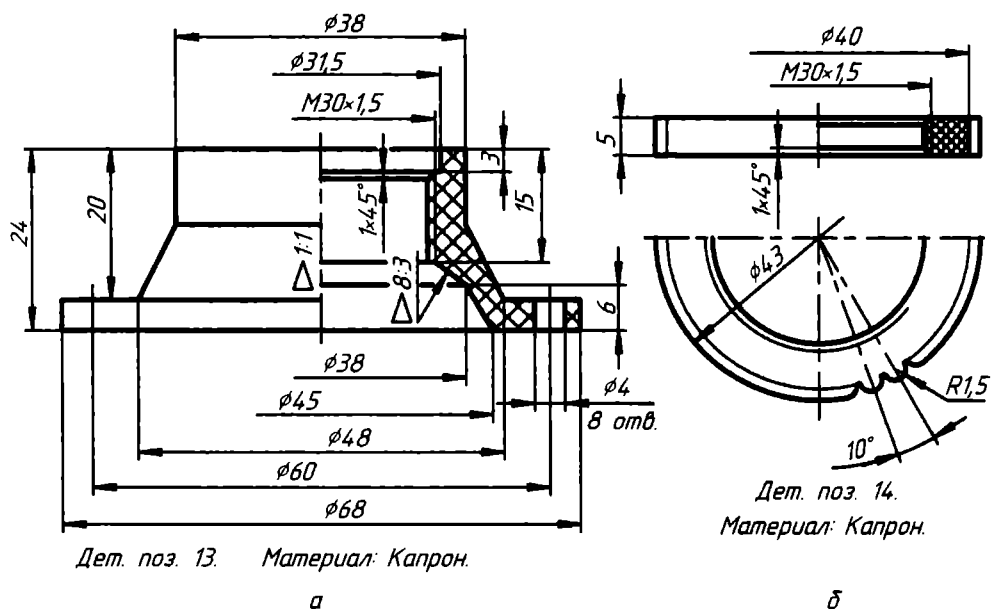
Чертежи: а — крышки; б — контргайки
